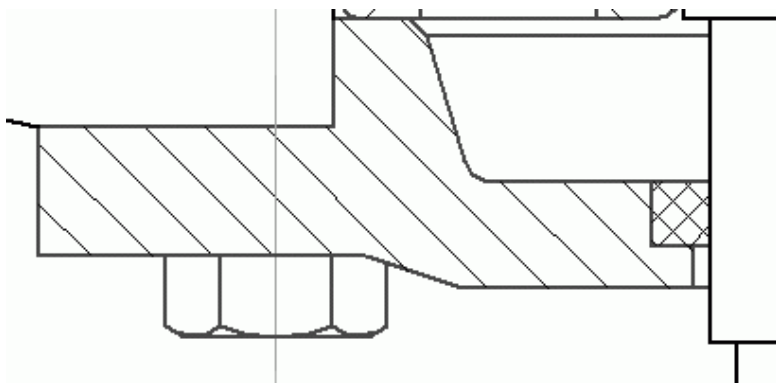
Фиксирующий винт сквозной крышки ведущего вала
